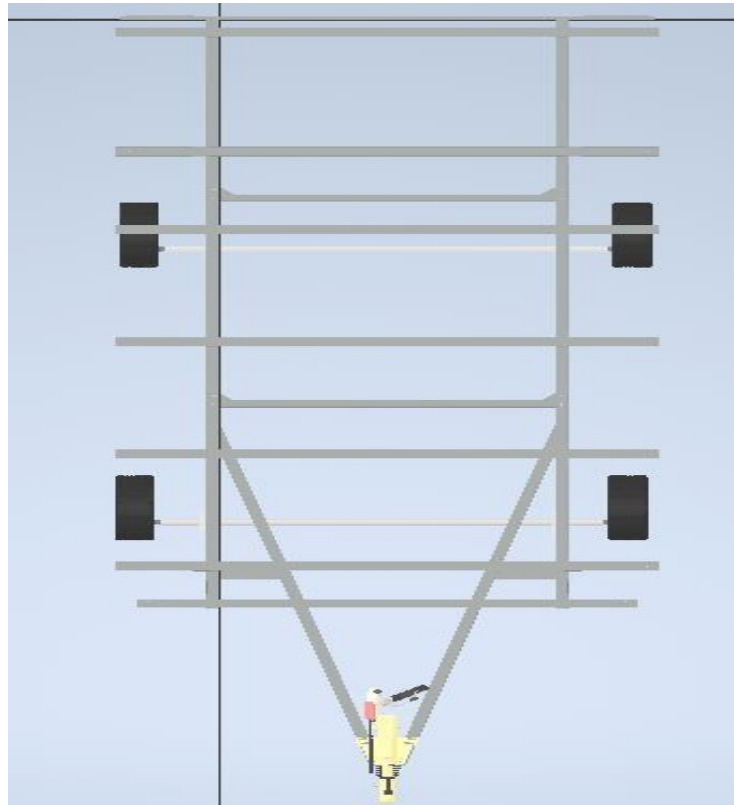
Diseño Inicial del Remolque. “Vista superior”
